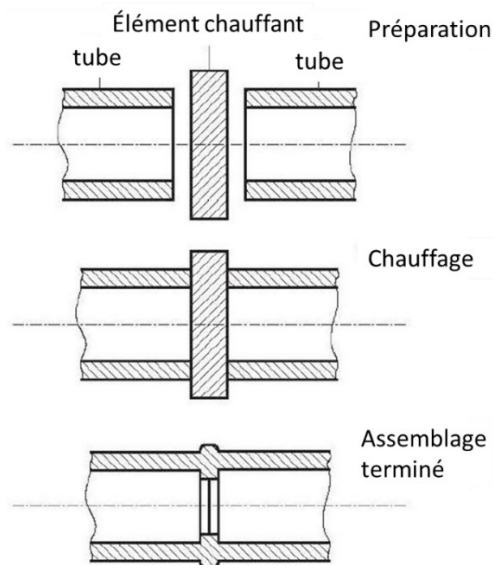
Déroulement schématique du soudage bout à bout par élément chauffant
